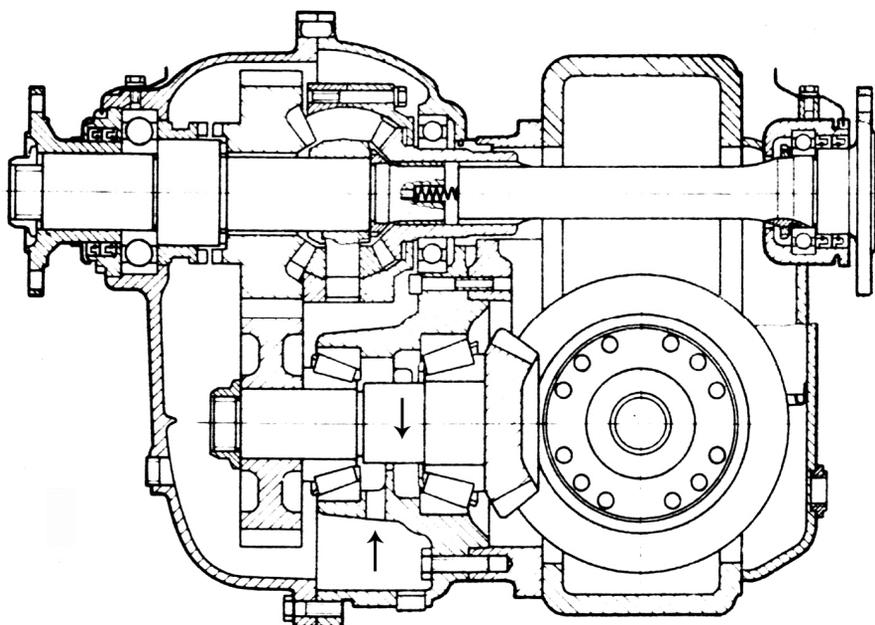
Схема подачи масла к подшипникам ведущей конической шестерни в проходных моста фирмы MAN первого поколения с разнесенной главной передачей
